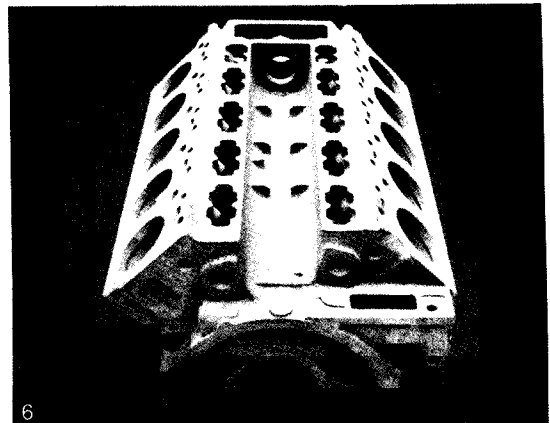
Sand-cast crank casing for V10 dissel engine.(weight : 193kg)
